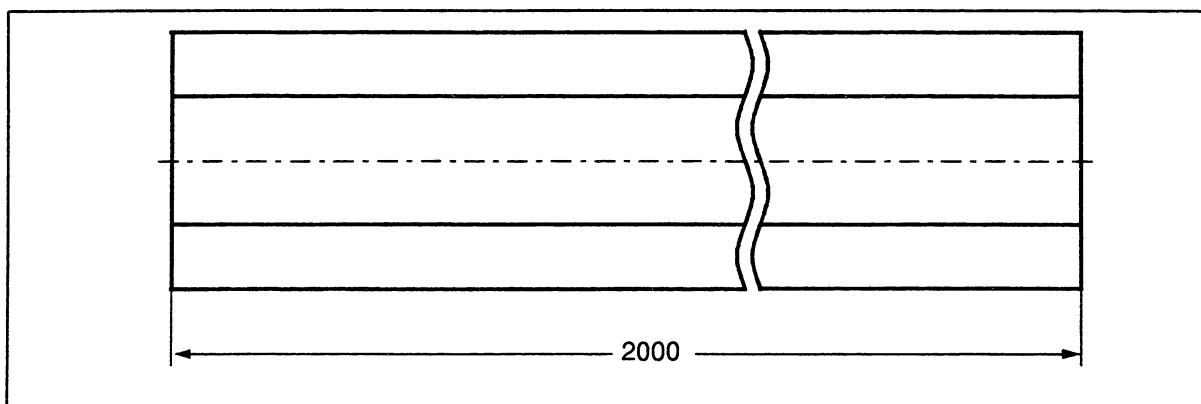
Plan d'encombrement du rail normalisé 2 m
